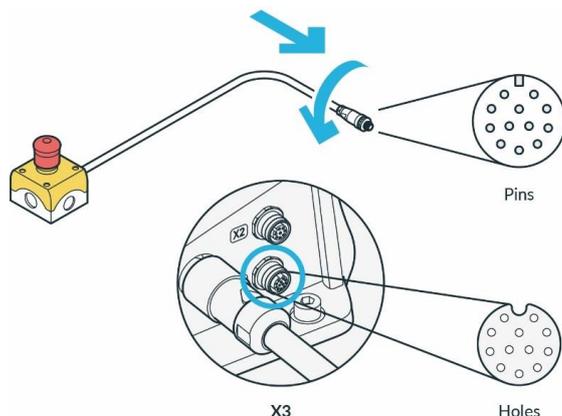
Collegamento del dispositivo di protezione (qui dispositivo di comando dell'arresto di emergenza)
